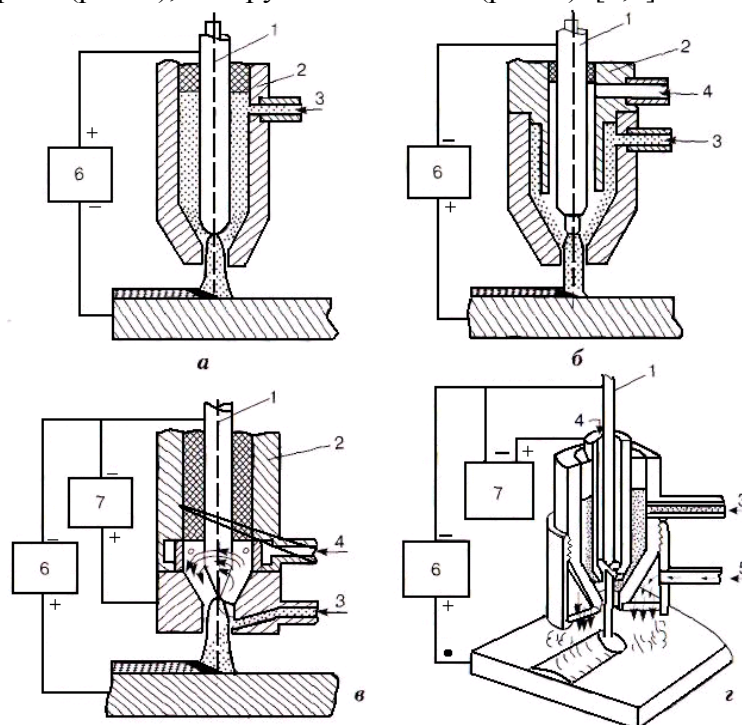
Схемы плазменной наплавки с вводом присадочного порошка в дугу внутри плазматрона: а — вместе с плазмообразующим газом; б — через электродную камеру; в — через боковое отверстие в канале сопла; г — через воронкообразную щель между соплами
